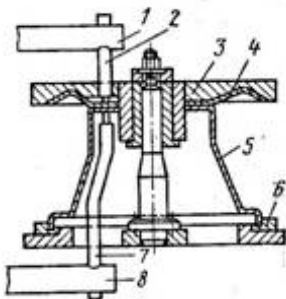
Кондуктор для сборки и прихватки втулок к цилиндрической обечайке:
